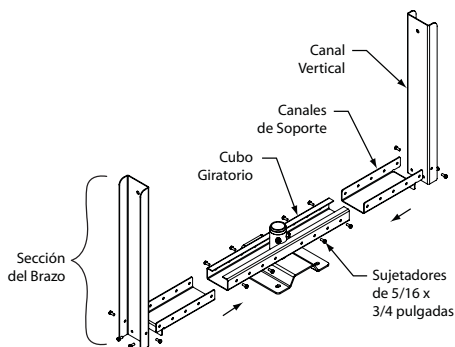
Conjunto de Soporte de Montaje en Cielo
